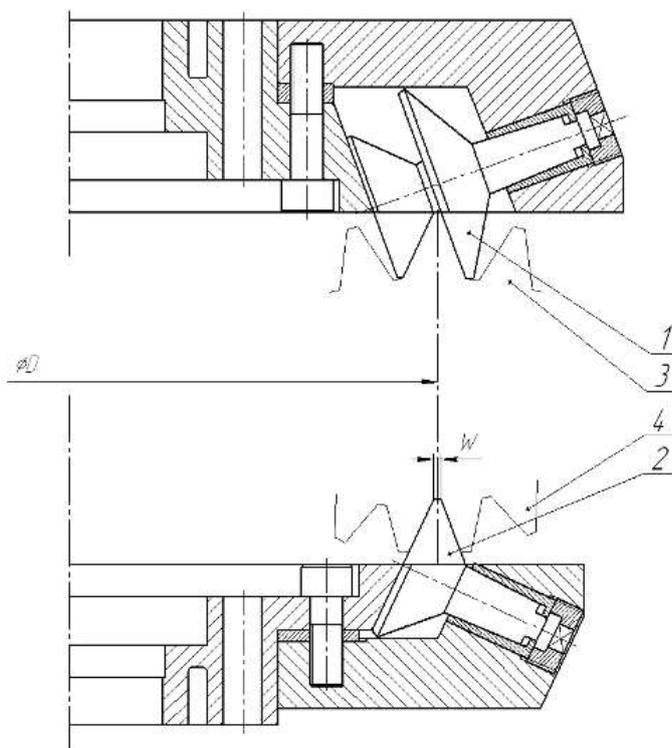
Предлагаемая конструкция зуборезной головки и схема нарезания колес обкатных передач
